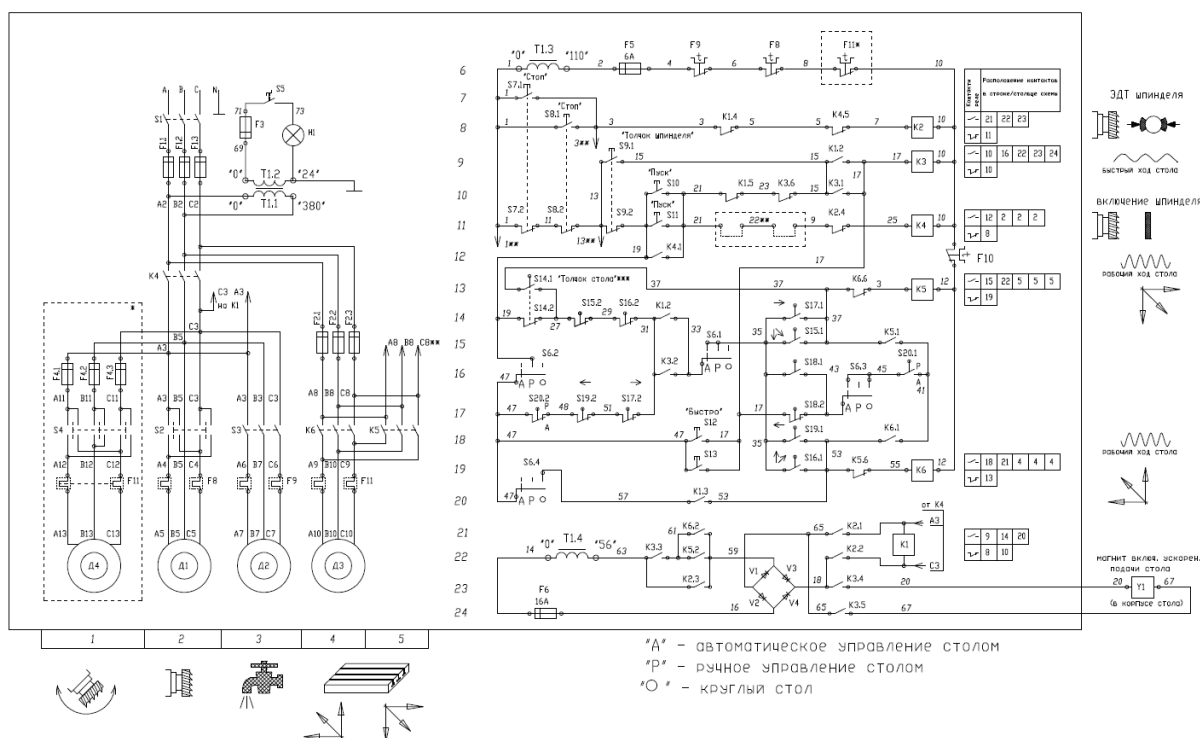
6P82Г. Консольно-фрезерный станок. Схема электрическая соединения.
